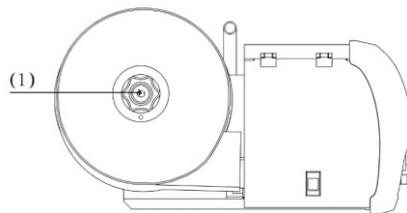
Регулировка усилия при торможении проволоки
